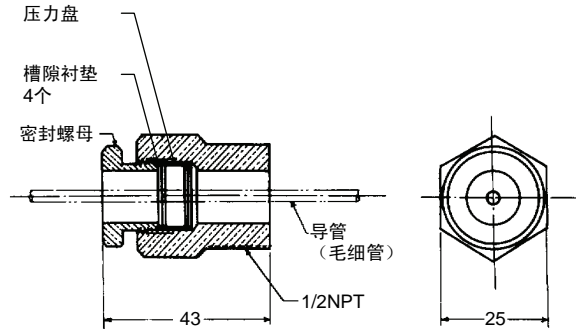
83165370-001 压力装配件 (另购品) 外形尺寸图
